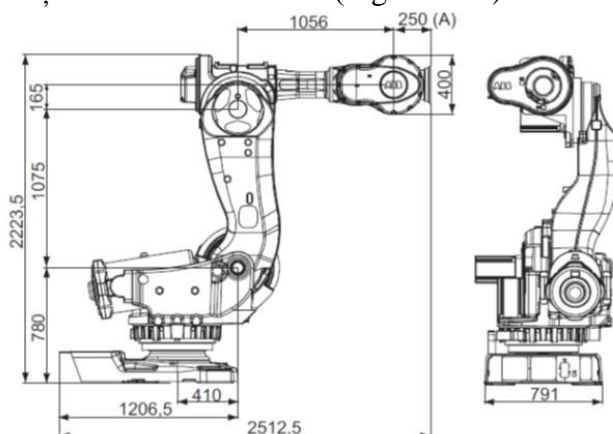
Schiță specificații dimensiuni robot ABB IRB 7600-500/2.55 [48]
